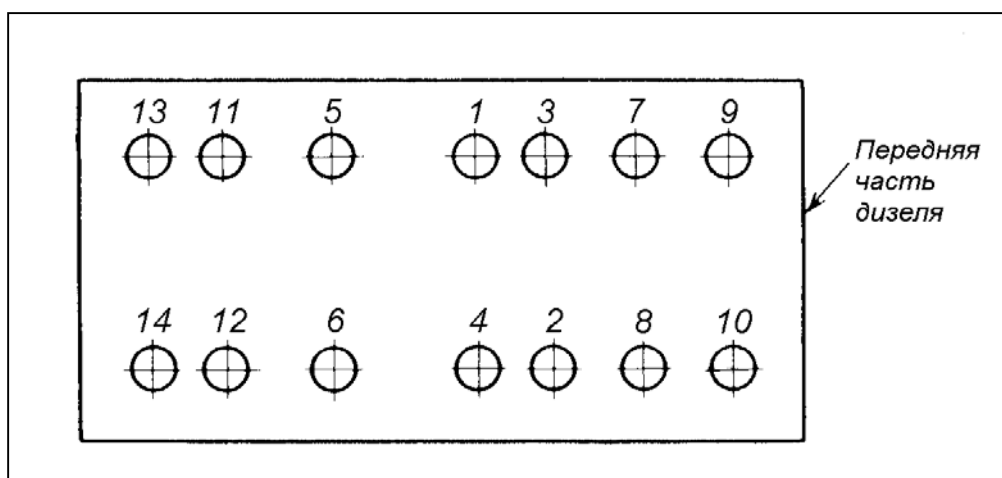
Схема затяжки гаек крепления коренных подшипников двигателей Д-108,-160 и модиф.
